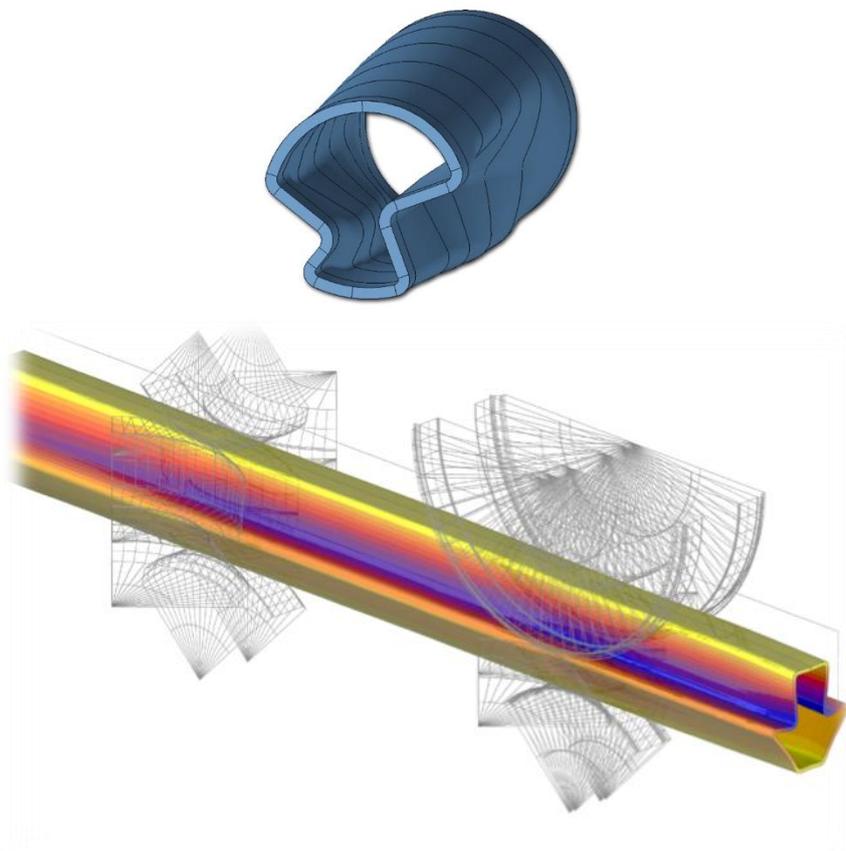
Формовка трубы сложного профиля из круглой заготовки
